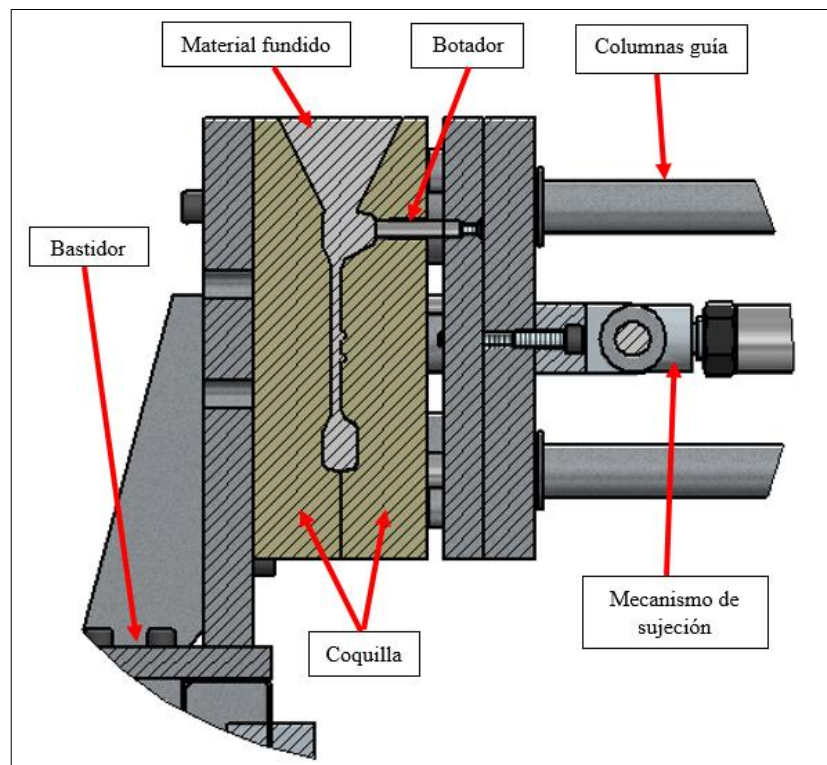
Coquilla para fundición de aluminio - Práctica UPS
